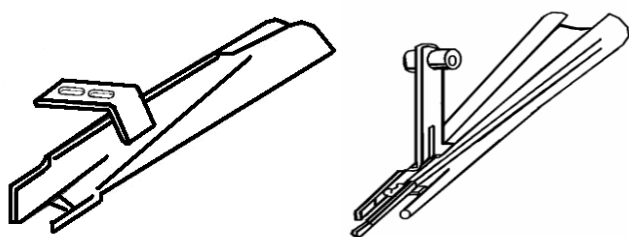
Спецприспособления для сборки прорезных карманов
